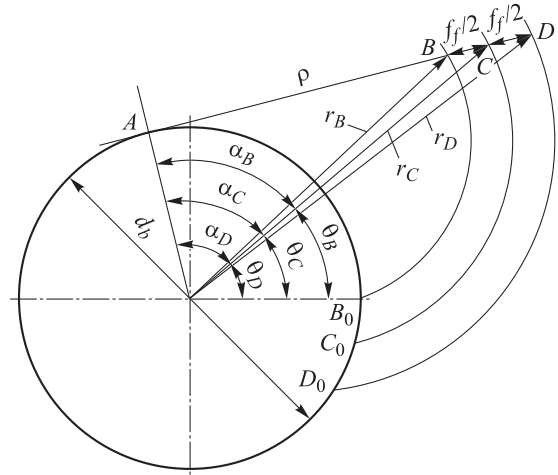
Расположение эвольвент окружностей в пределах поля допуска f_f
